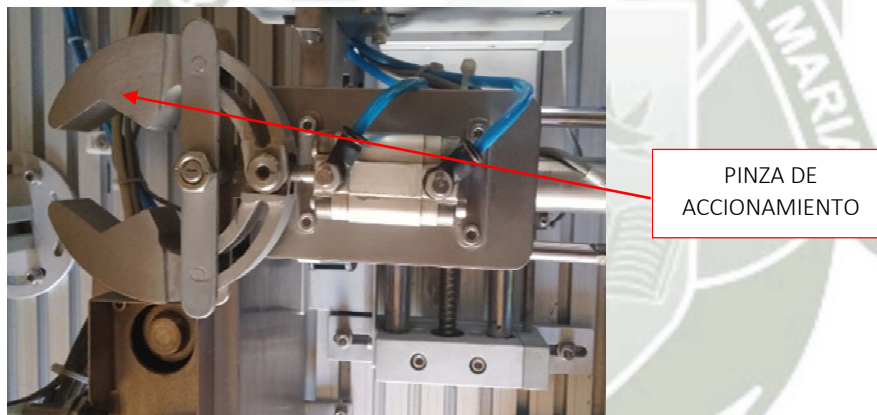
Cilindro compacto de doble efecto – Actuador 3
